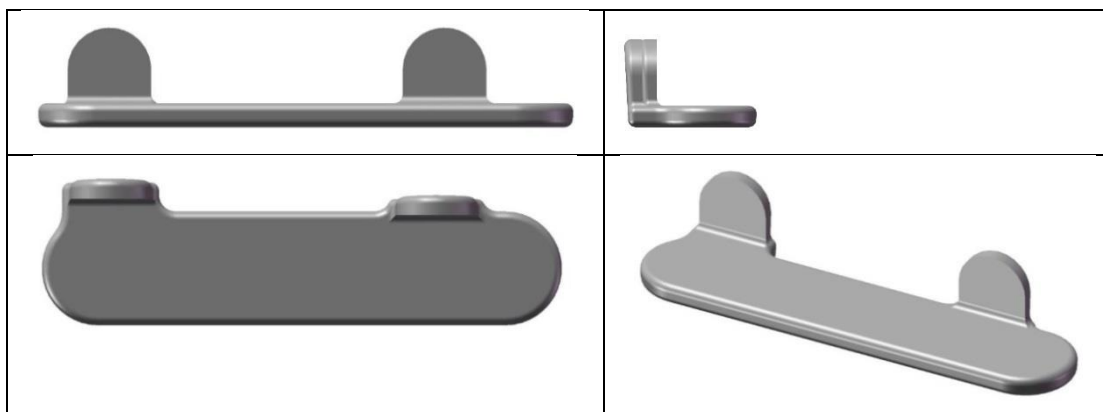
Компьютерная 3D-модель заготовки детали «Серьга»
